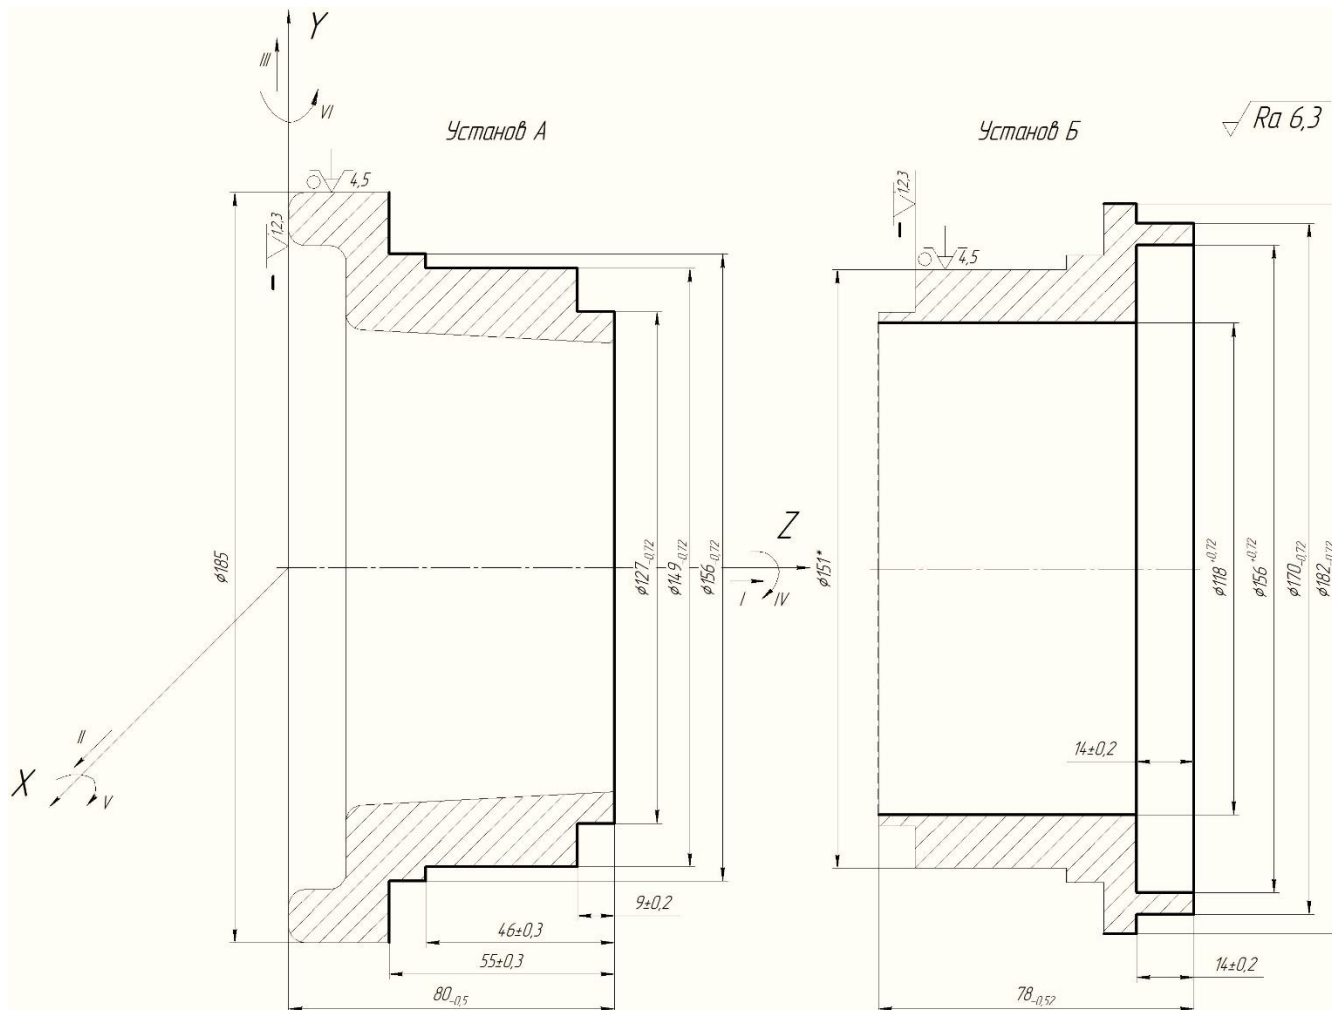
Схема установки заготовки на токарній операції (варіант 1)
